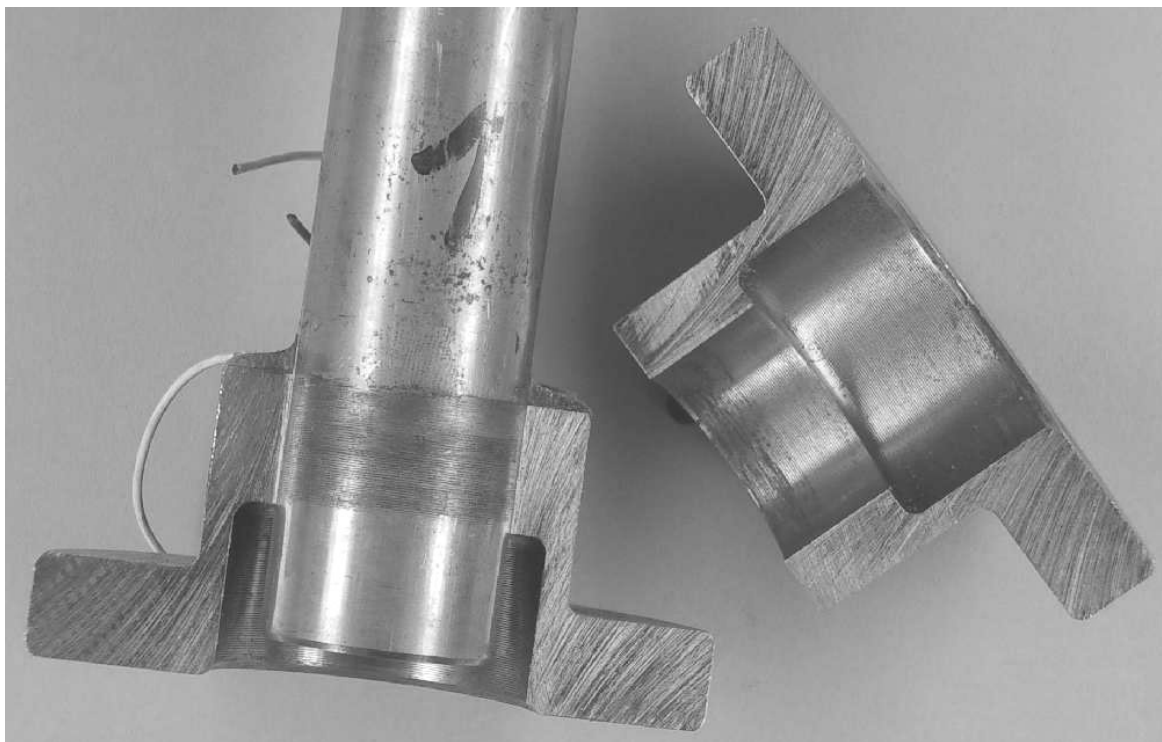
Torsionsbeanspruchte, innenhochdruckgefügte Welle-Nabe-Verbindung
